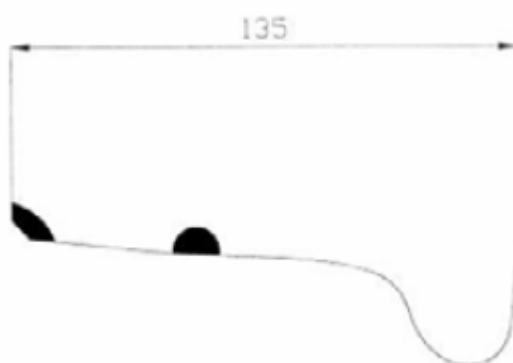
Zona de localización de fisuras térmicas en la llanta (medidas en mm).
